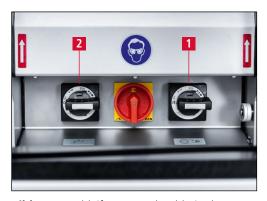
Schleifmotor und Kühlmitteleinrichtung einschalten
